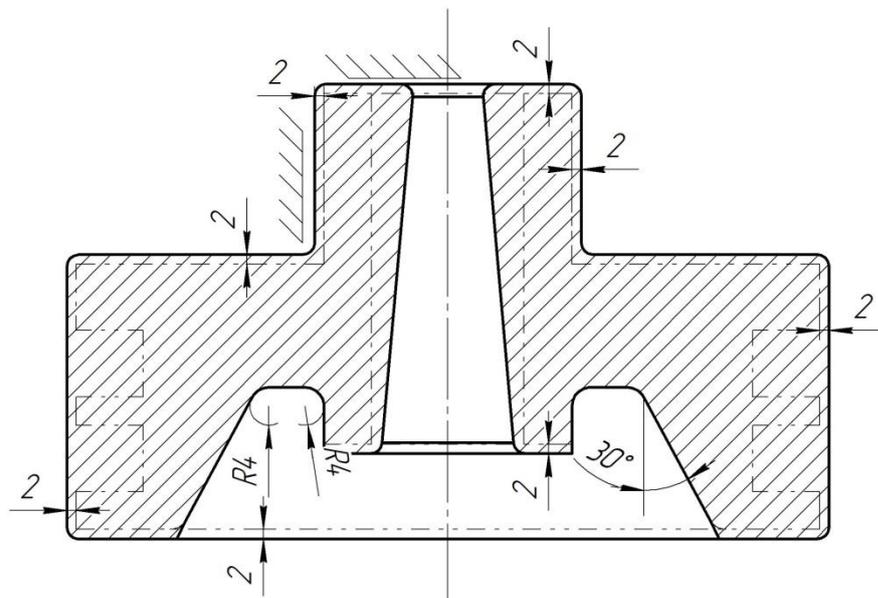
Общий вид заготовки детали - «Поршень»
